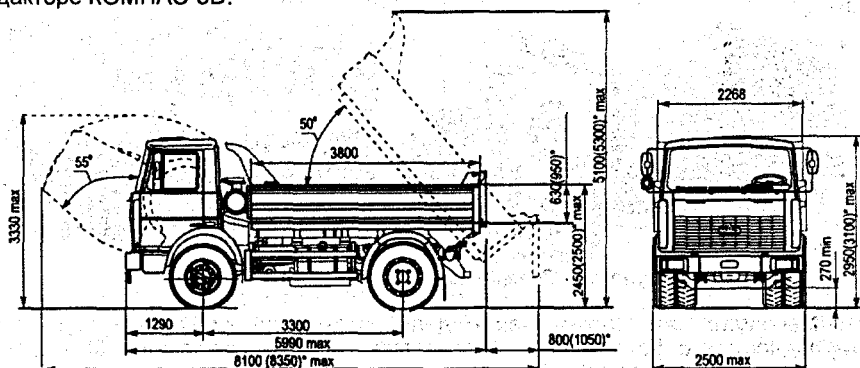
Основные размеры грузового автомобиля МАЗ-5551
